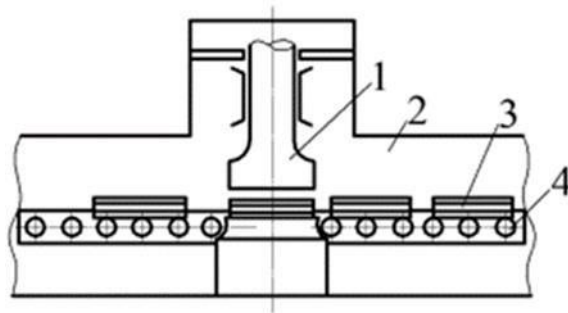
Схема установки для потокового осаджування біметалевих пакетів у печі: 1 – бойок преса; 2 – робочий простір печі; 3 – біметалеві пакети; 4 – рольганг [13]
